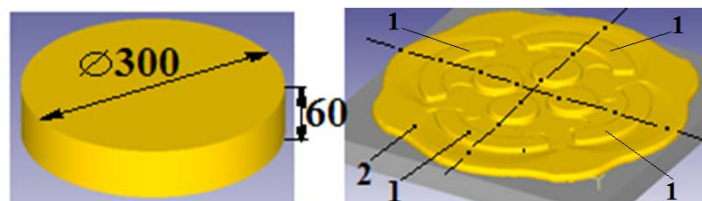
Многоступенчатая штамповка: (1 – поковки; 2 – облой)
